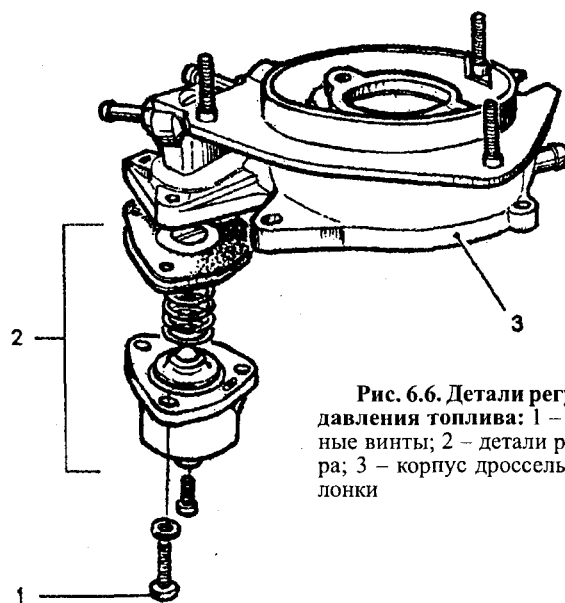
Детали регулятора давления топлива: 1 – крепежные винты; 2 – детали регулятора; 3 – корпус дроссельной заслонки
